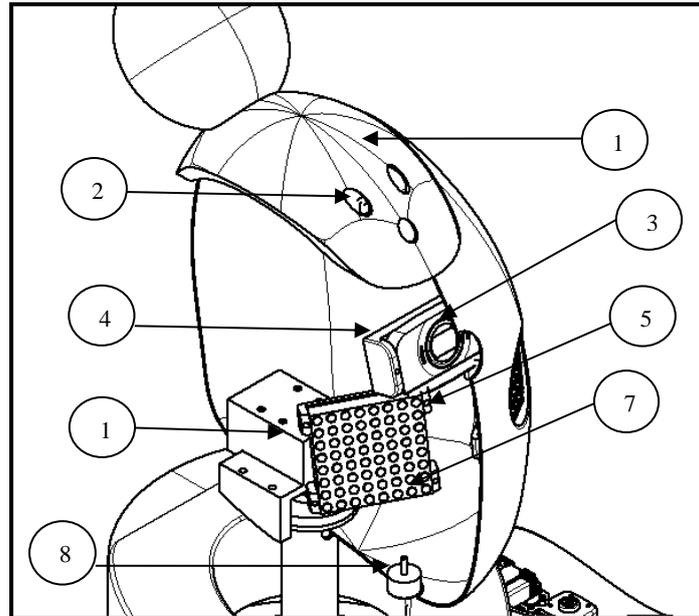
Vista isométrica del interior de la Cabeza del robot (Fuente: Propia)
